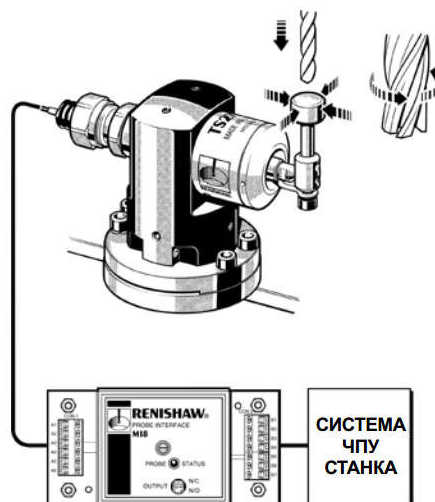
Система контроля датчиком состояния режущего инструмента ЧПУ
